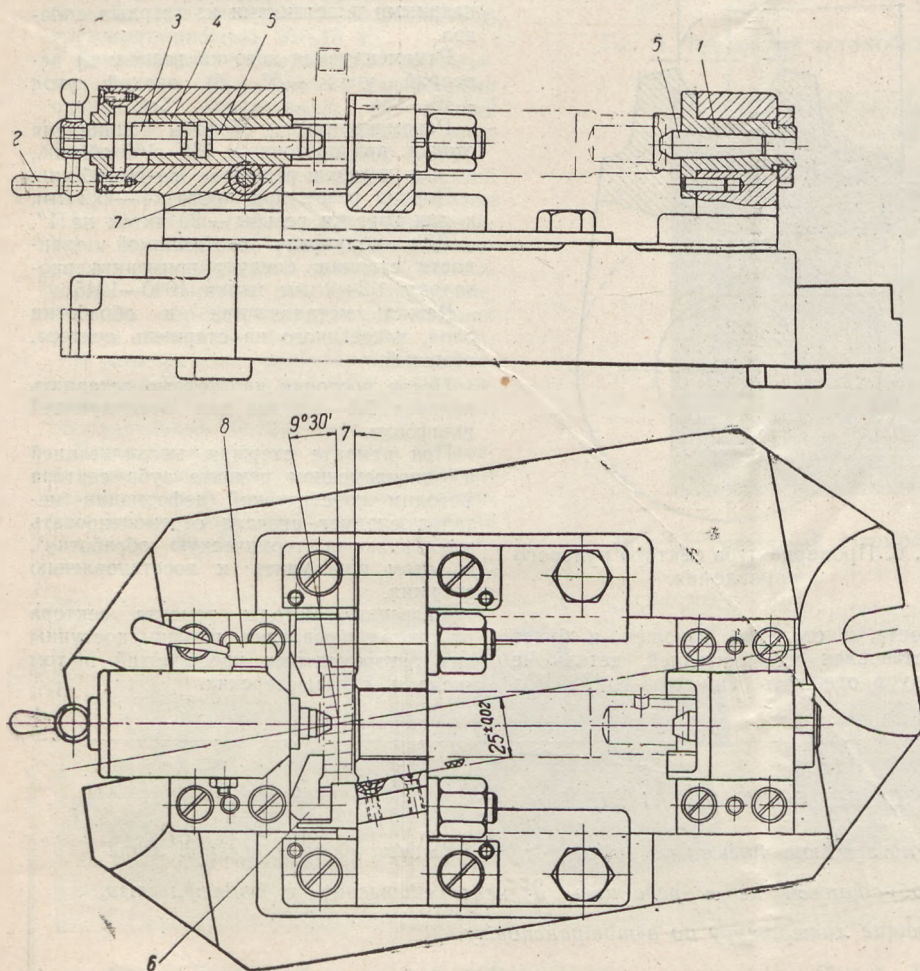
Приспособление для фрезерования зуба в секторе рулевого управления.
